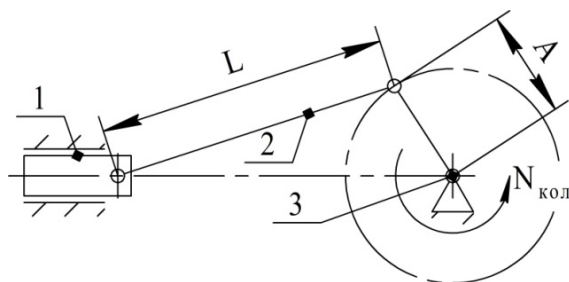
Кинематическая схема механизма поперечных колебаний электродного узла сварочного автомата:
